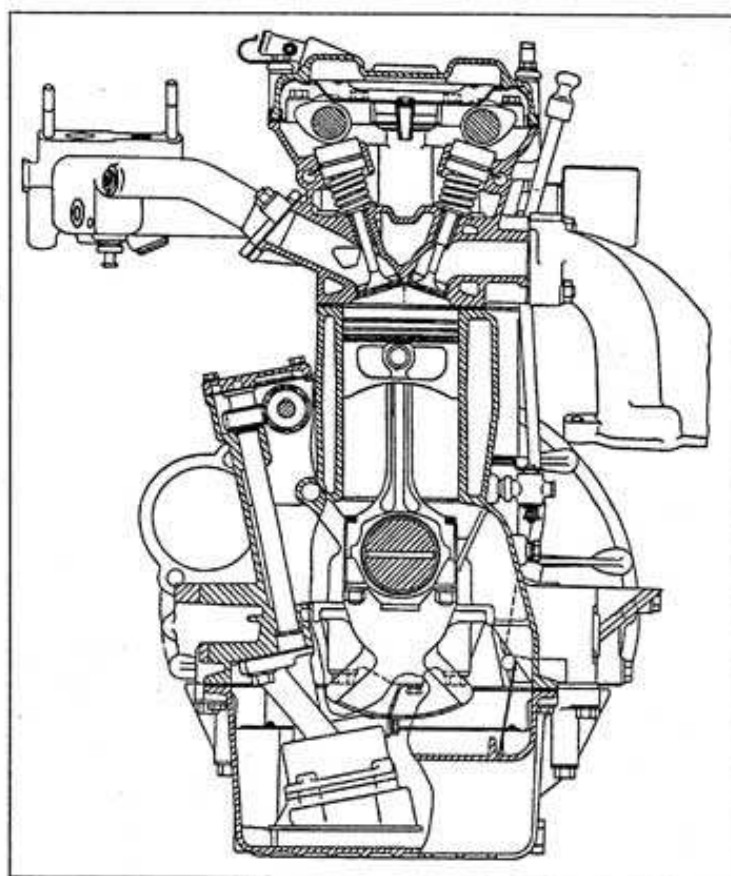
Поперечный разрез двигателей ЗМЗ-4061, -4063
